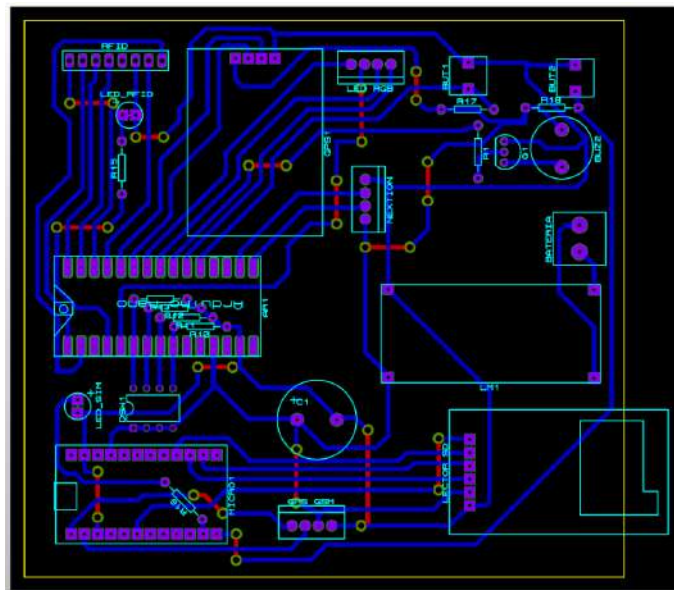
Diseño de la placa PCB para el prototipo
